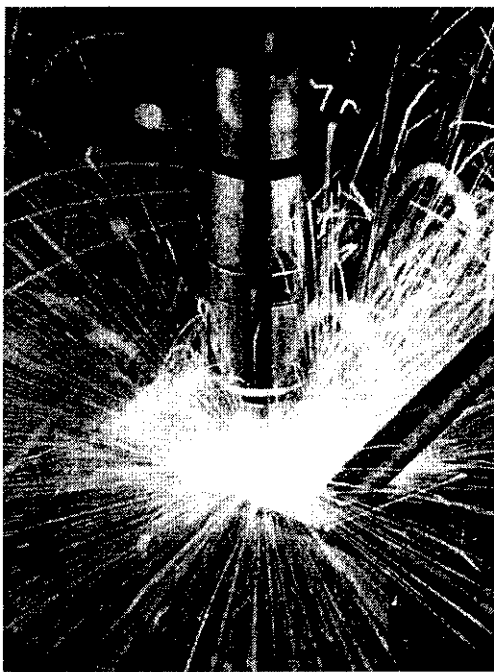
Proceso de soldadura por descarga de condensadores
